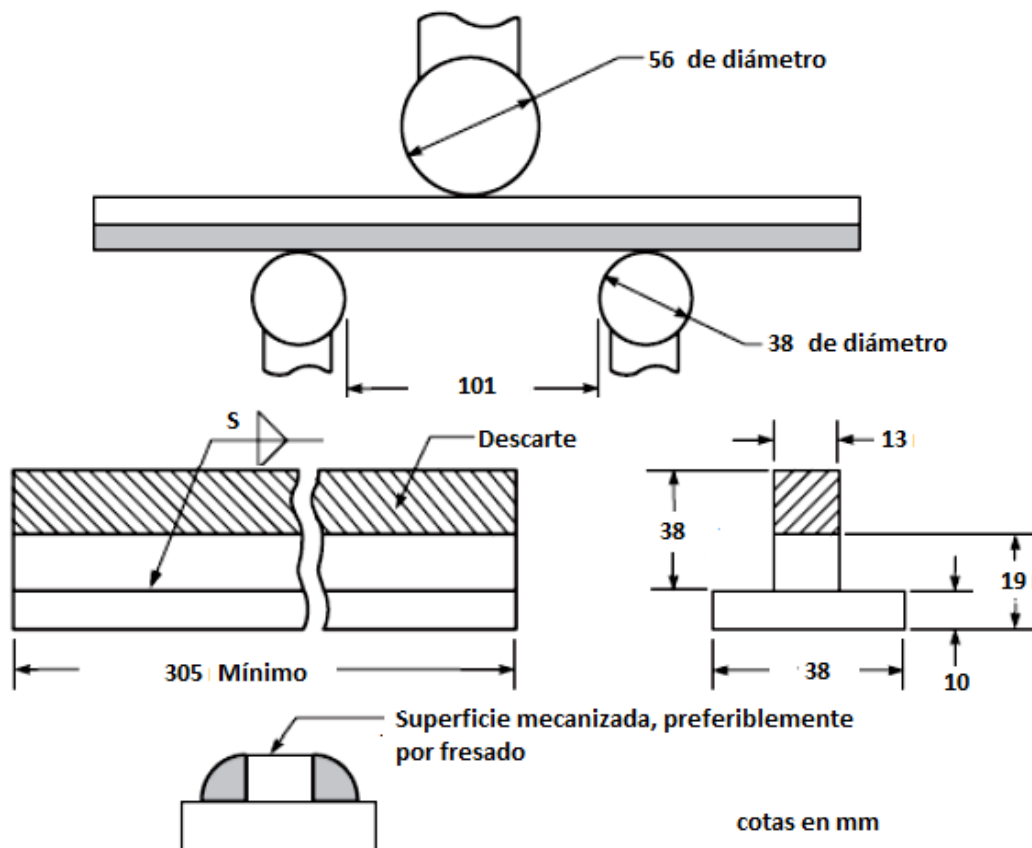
Probeta longitudinal para curvatura de soldadura de filete [3].
